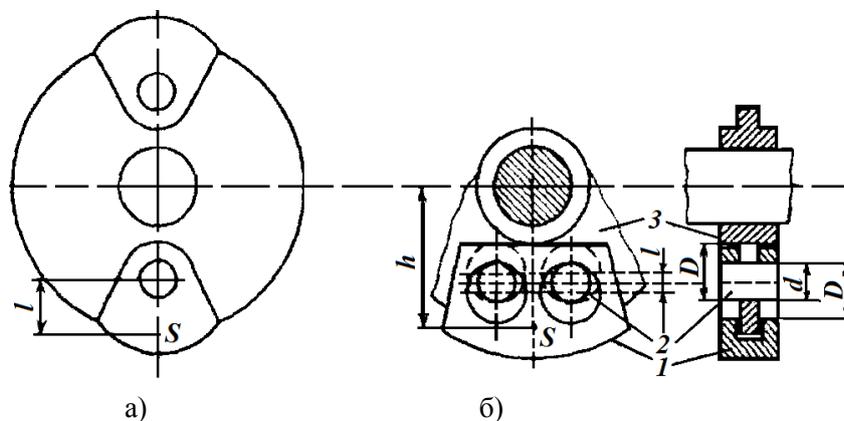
Конструкция центробежного маятникового виброгасителя крутильных колебаний вала
